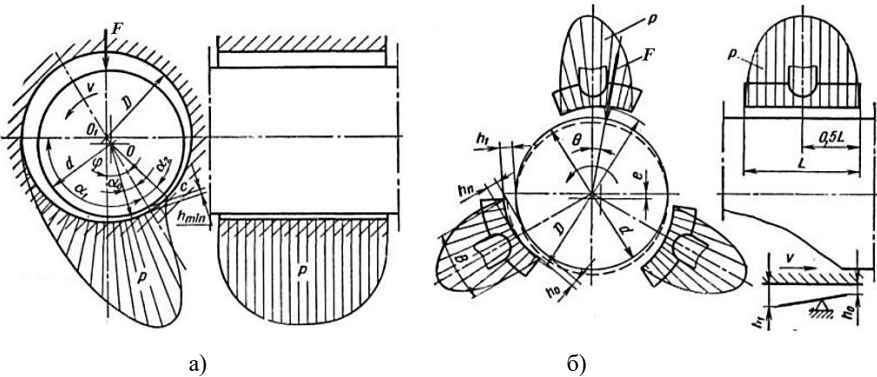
Схема гідродинамічного підшипника: а – одноклинового; б - багатоклинового
